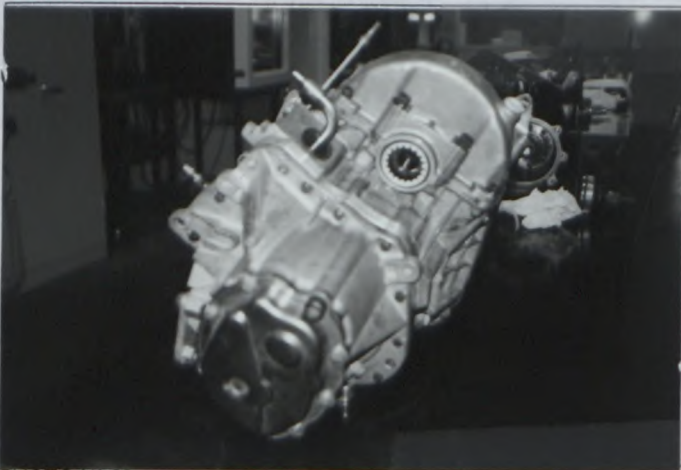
( B. V. 6 ou 7 vitesses )
